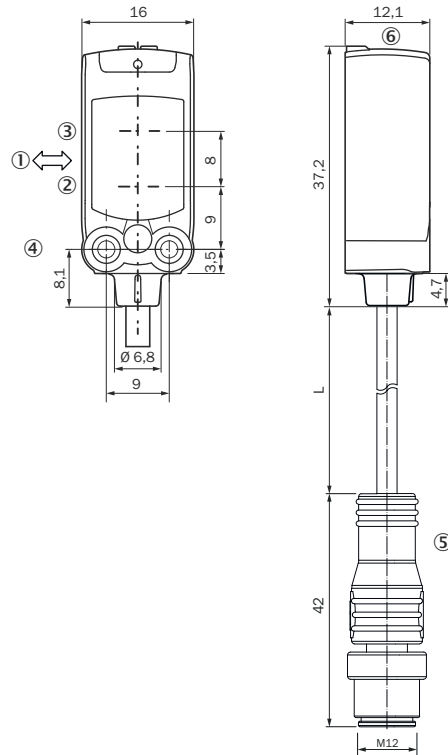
Desenho dimensional 1, cabo com conector macho M12
